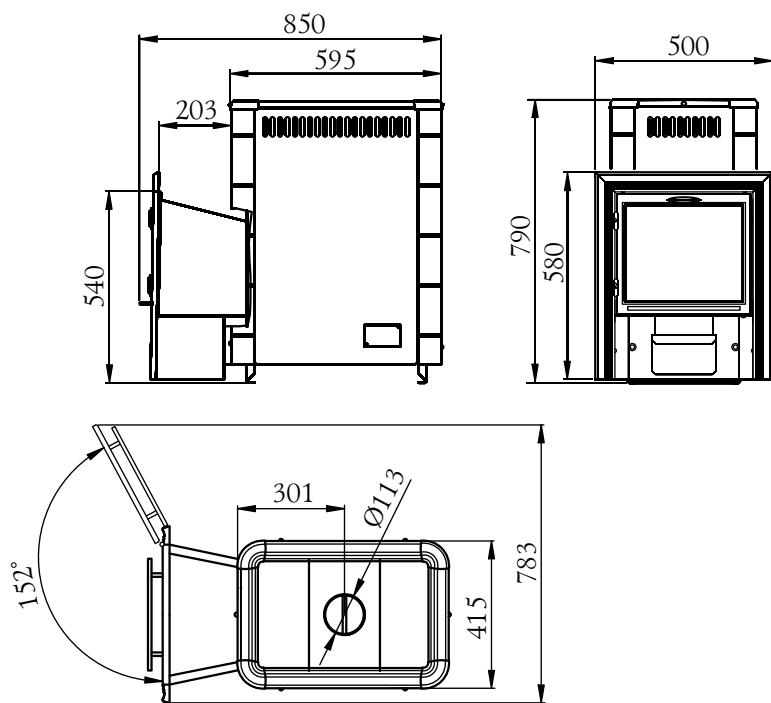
Габаритные размеры печи «Ангара Витра».
